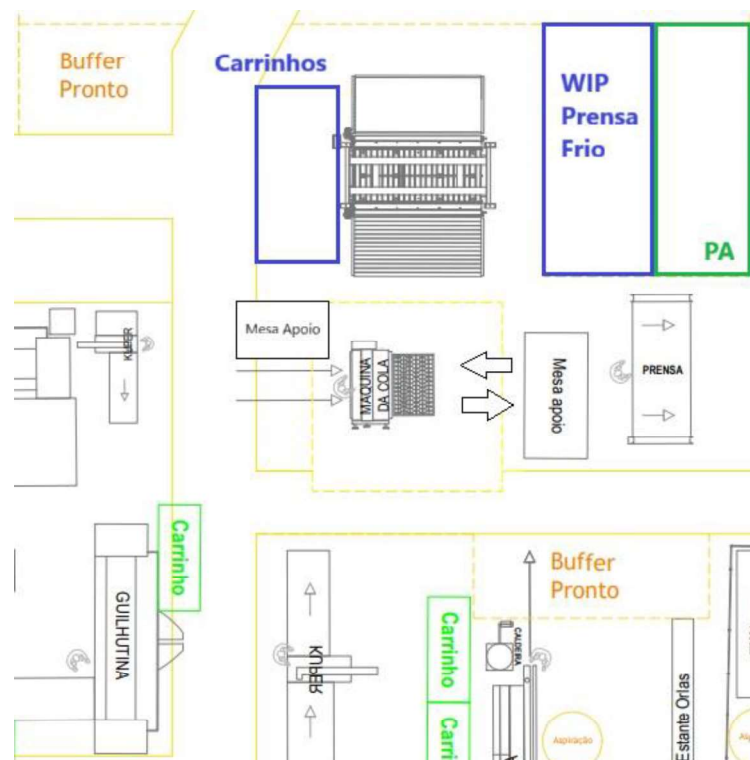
Esboço de layout proposto para a Aplicação de Folha
